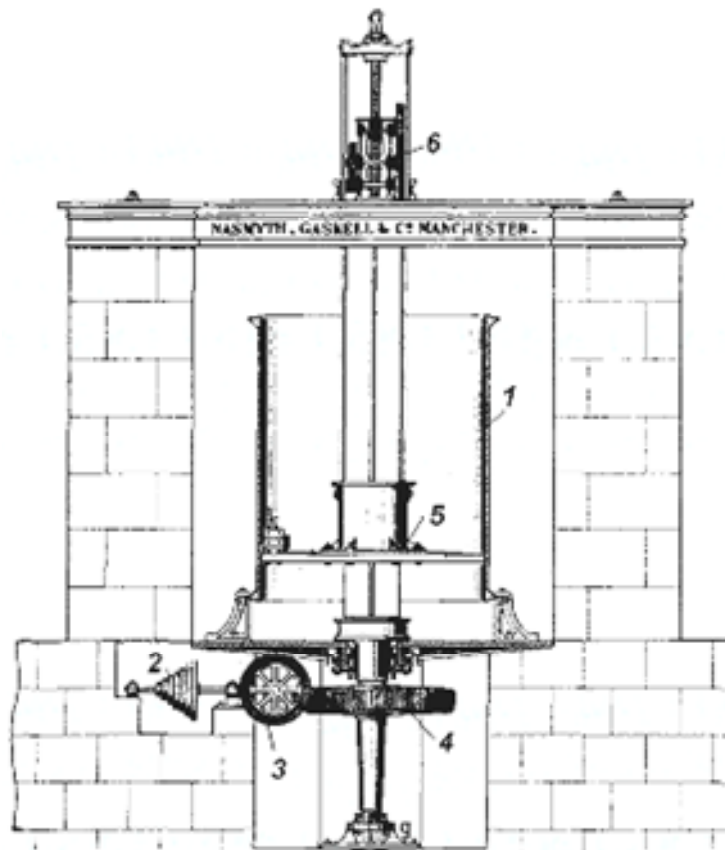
Тяжелый станок для расточки уникальных цилиндров паровых машин (конструктор Дж. Несмит, 1841 г.)
